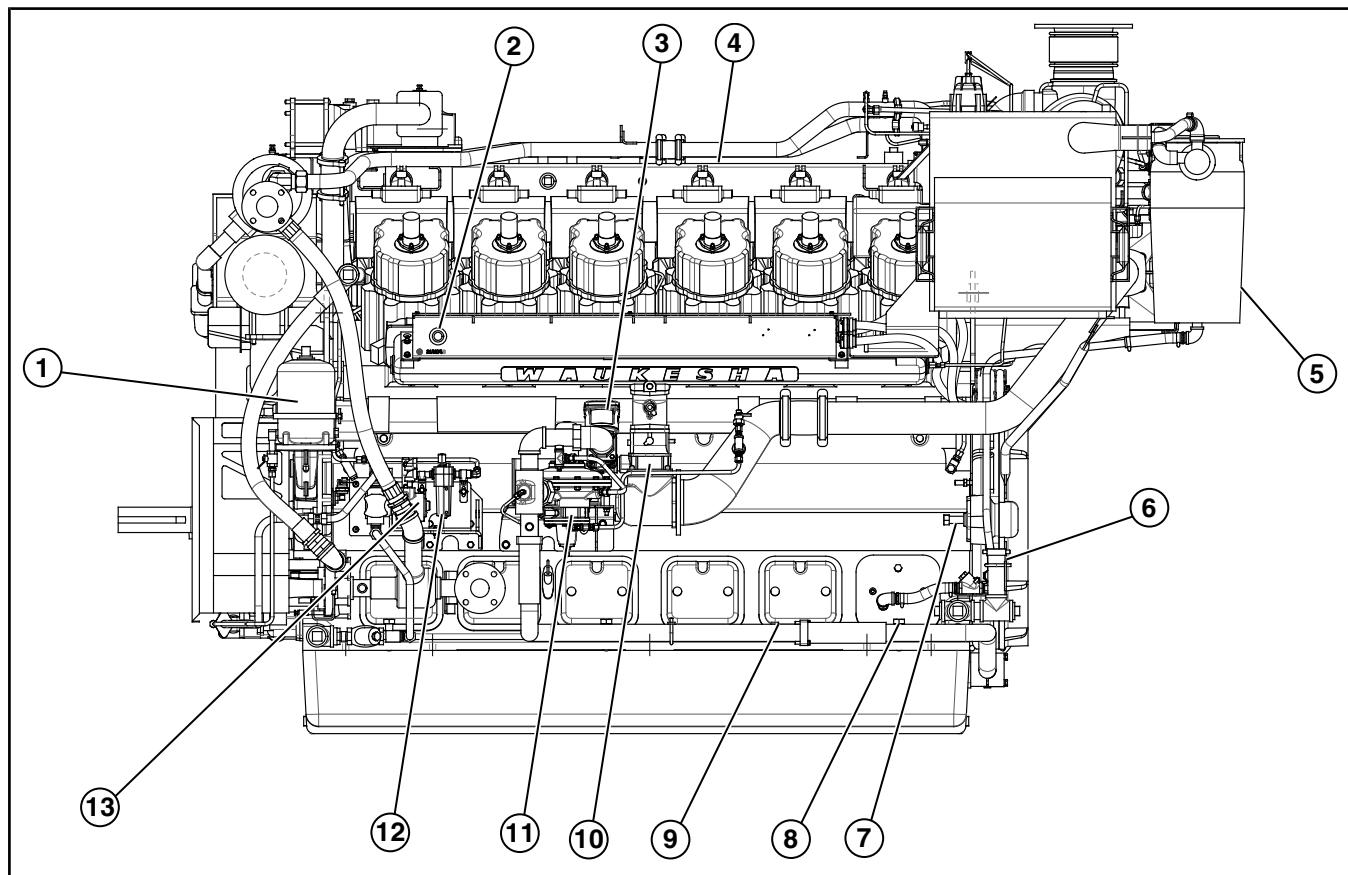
Вид слева (двигатель L7044GSI)
